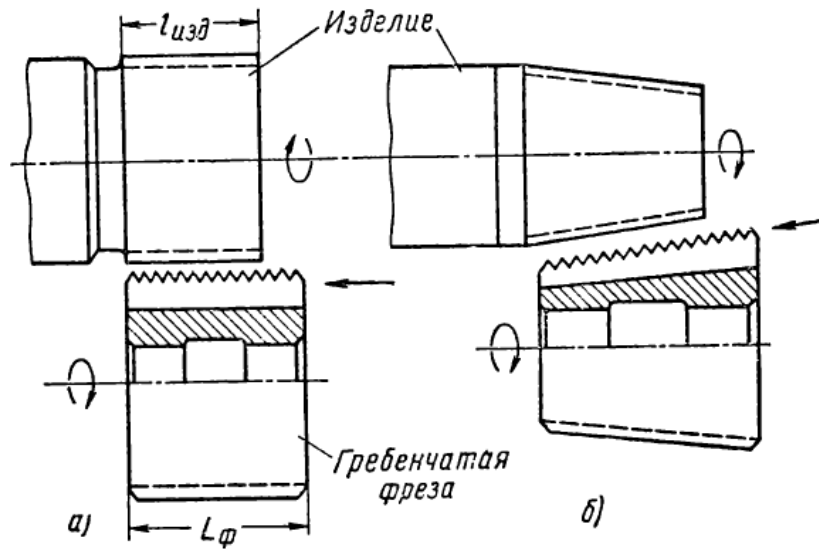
Схема фрезерування різьби багатонитковими (гребінчастими) різьбовими фрезами
